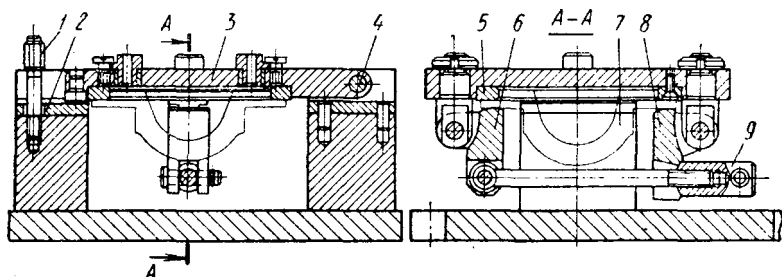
Приспособление для обработки отверстий в мелких крышках
